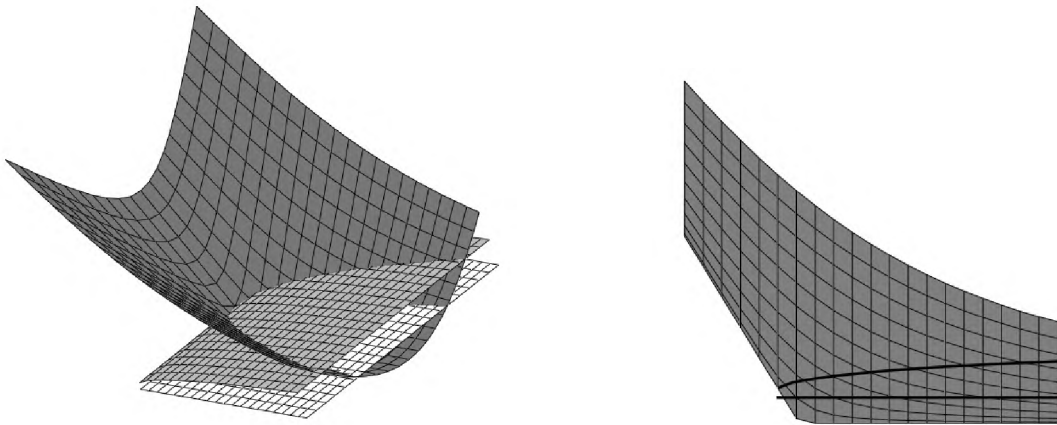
Взаємне розташування поверхонь інструменту, нездеформованої заготовки та найвищого положення гребінця хвилі
